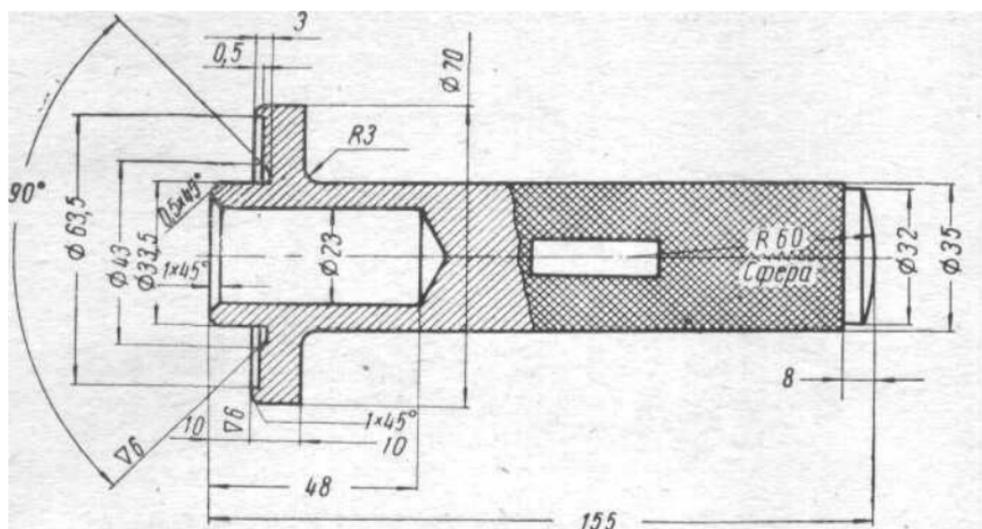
Оправка для запрессовывания сальника в горловину картера редуктора
